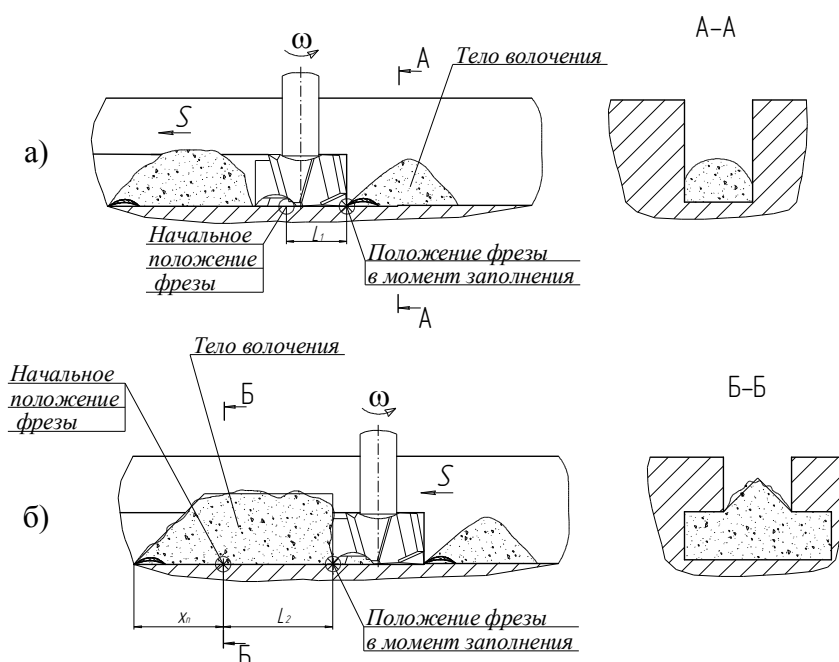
Схема заполнения стружкой пазов при их фрезеровании: а) прямоугольного паза; б) Т-образного паза
